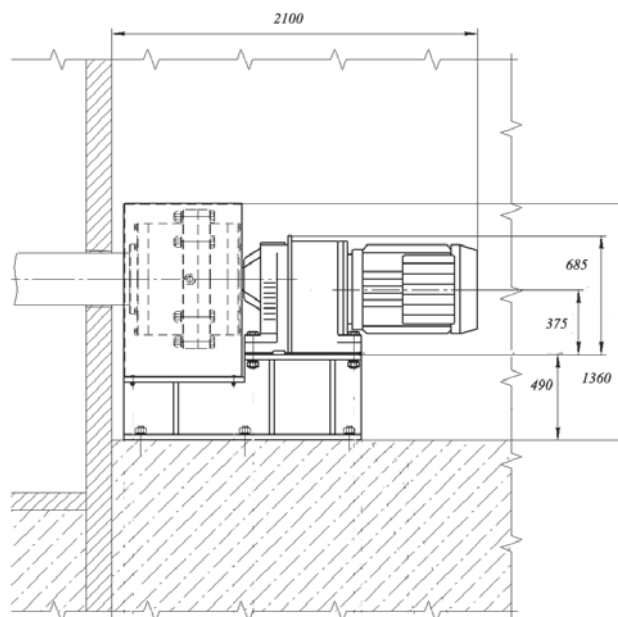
Общий вид приводной части шаровой мельницы после реинжиниринга
